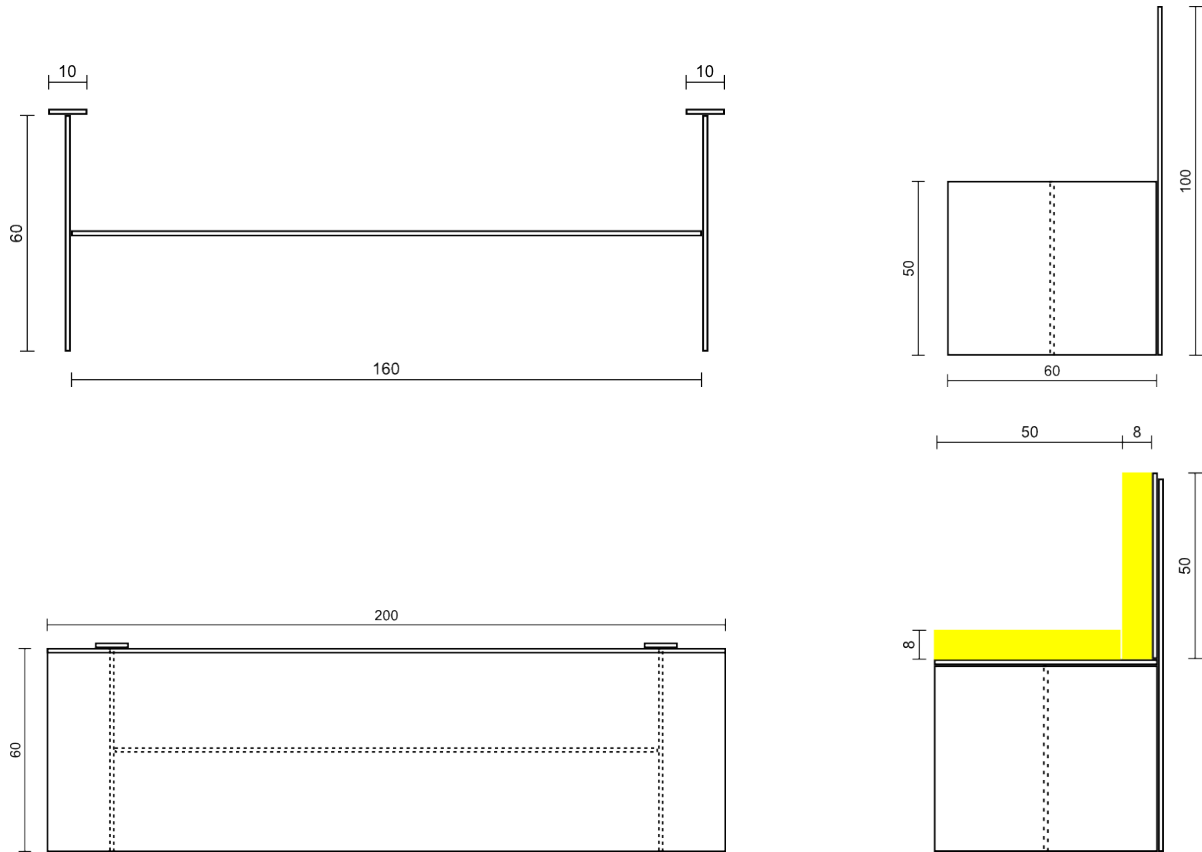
Konstruktion der Sofas, Abmessungen in cm (links oben: Gestell Draufsicht; rechts oben: Gestell Seitenansicht; links unten: Auflagen Draufsicht; rechts unten: Auflagen Seitenansicht)
